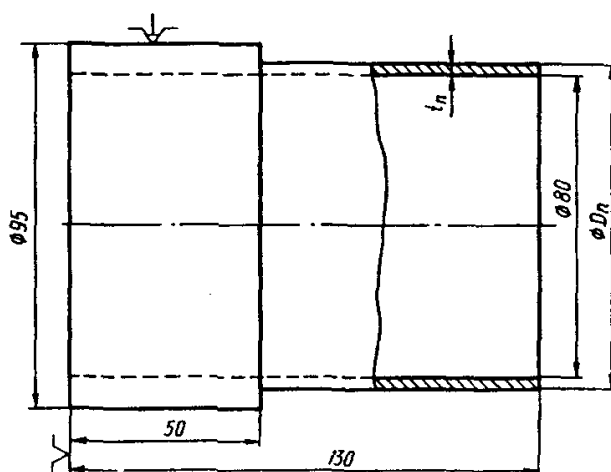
Схема закрепления тонкостенной заготовки
